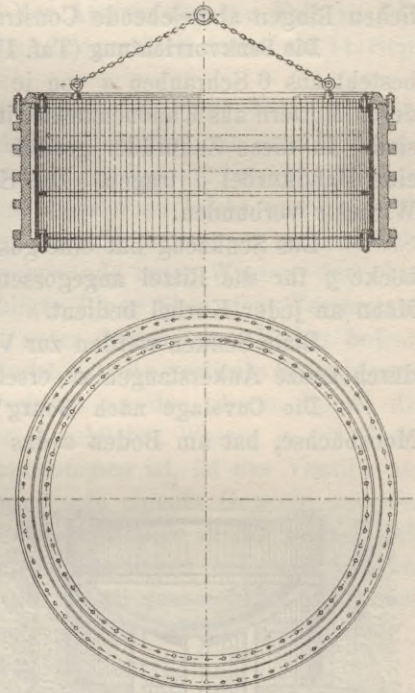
Presskübel für die Druckprobe von Cuvelage-Ringen M. 1 : 100.
